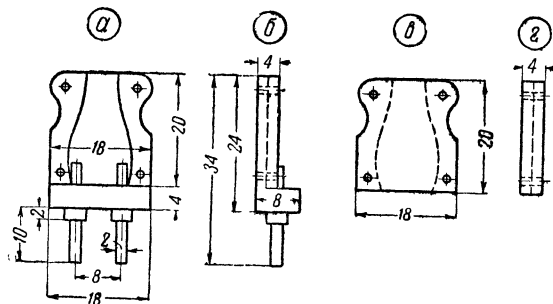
Детали двухполюсной вилки: а — основание (вид спереди); б — основание (вид сбоку); в — крышка (вид спереди); г — крышка (вид сбоку)
